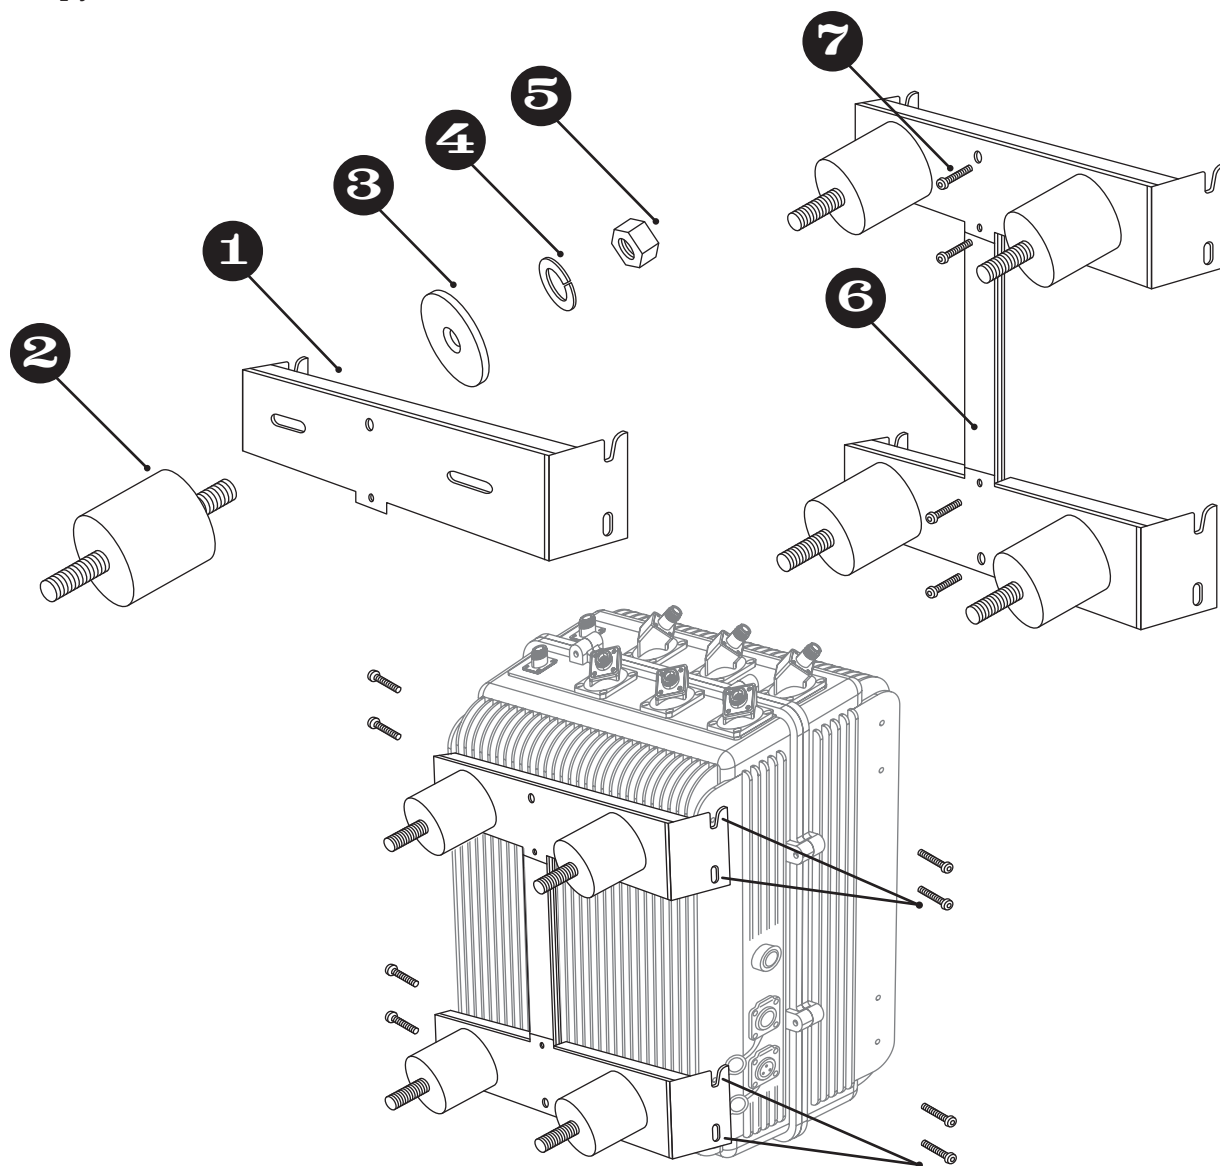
Комплектующие для сборки соединительного крепления подавителя
